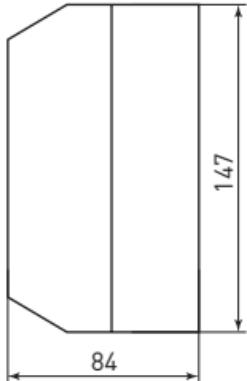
Габаритные размеры защитной монтажной коробки (IP41)
